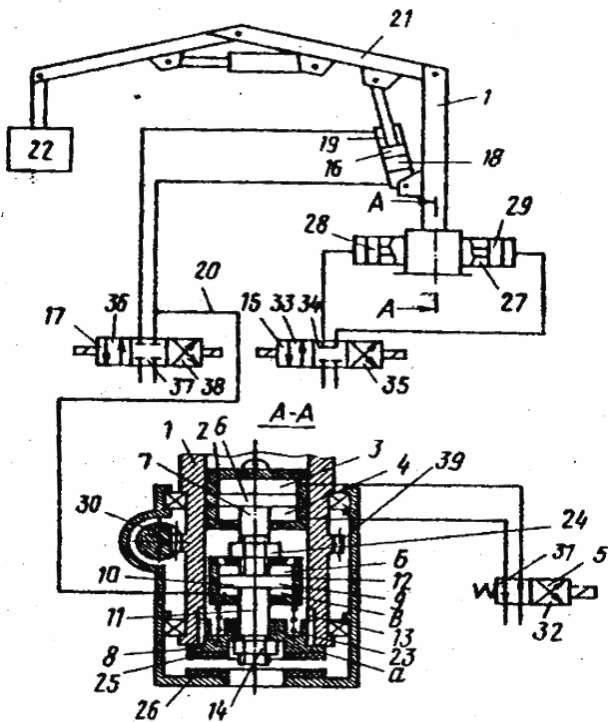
Поворотний пристрій маніпулятора: 1 – стоек; 2 – гідроциліндр гальмівного пристрою; 3, 4 – поршнева і штокова порожнини; 5 – розподільник; 6, 7 – поршень і шток гідроциліндра гальмівного пристрою; 8 – повзун; 9, 10, 11, 12 – складові частини додаткового гідроциліндра; 13 – шліцевий паз; 14, 24 – різьбові гайки; 15, 33, 35 – розподільник поворотного гідроциліндра; 16, 18, 19 – гідроциліндр підйому стріли; 17, 36, 37, 38 – розподільник гідроциліндра підйому; 20 – гідролінія; 21 – стріла; 22 – вантаж; 23 – пружина; 25, 26 – фрикційні диски; 30 – зубчаста рейка; 31, 32 – розподільник; 39 – зубчастий вінець
